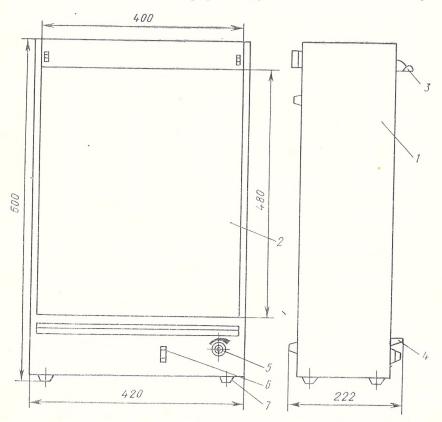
Негатоскоп общего назначения H-48 1 — корпус, 2 — экран; 3 — кронштейн; 4 — лоток; 5 — ручка регулировки яркости; 6 — выключатель; 7 — ножка.
